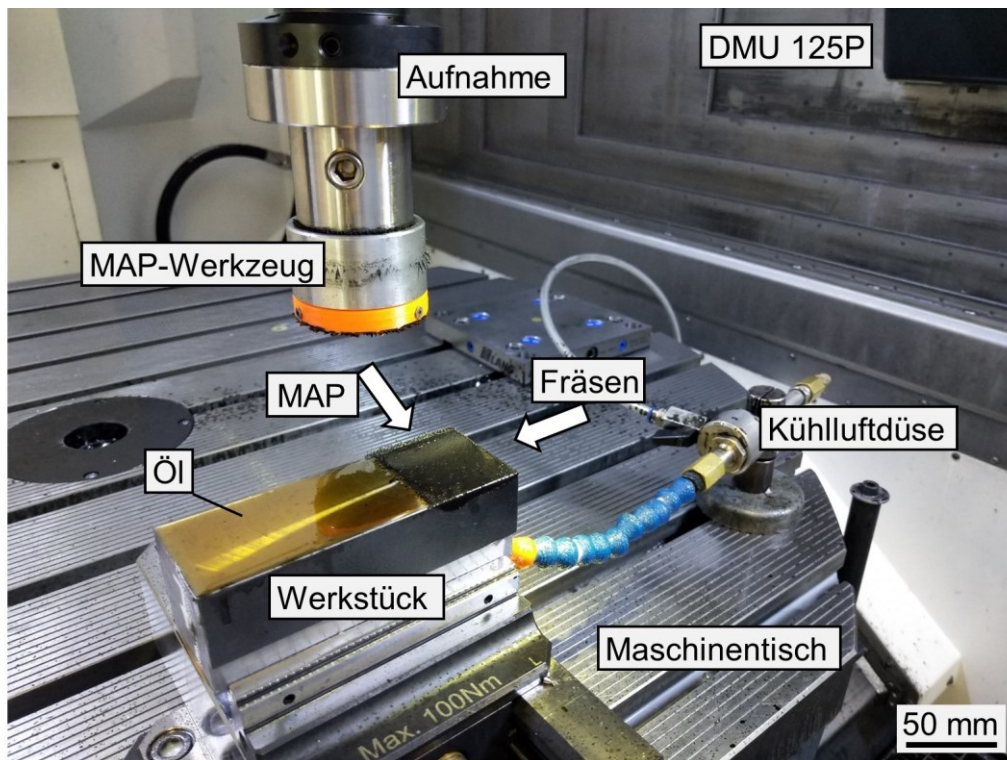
Versuchsstand für das magnetabrasive Polieren an der Werkzeugmaschine DMU Ultrasonic 125 P
